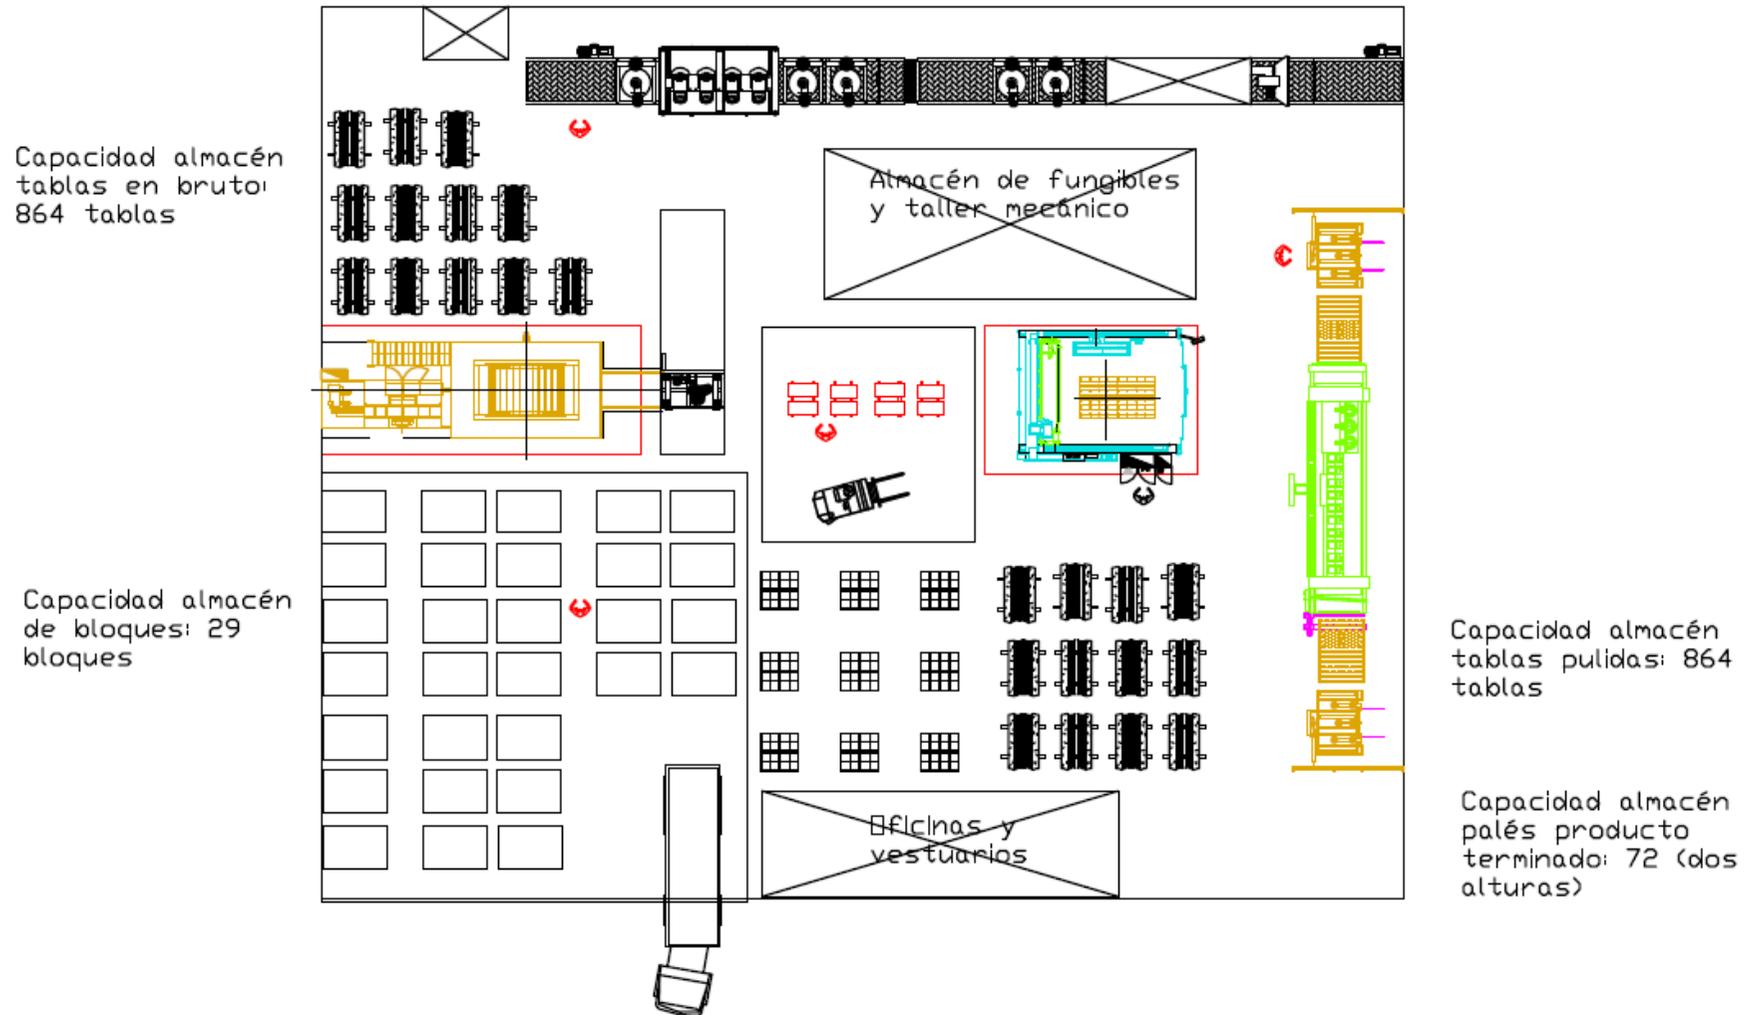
Layout de una instalación industrial modelo de elaboración de piedra natural
